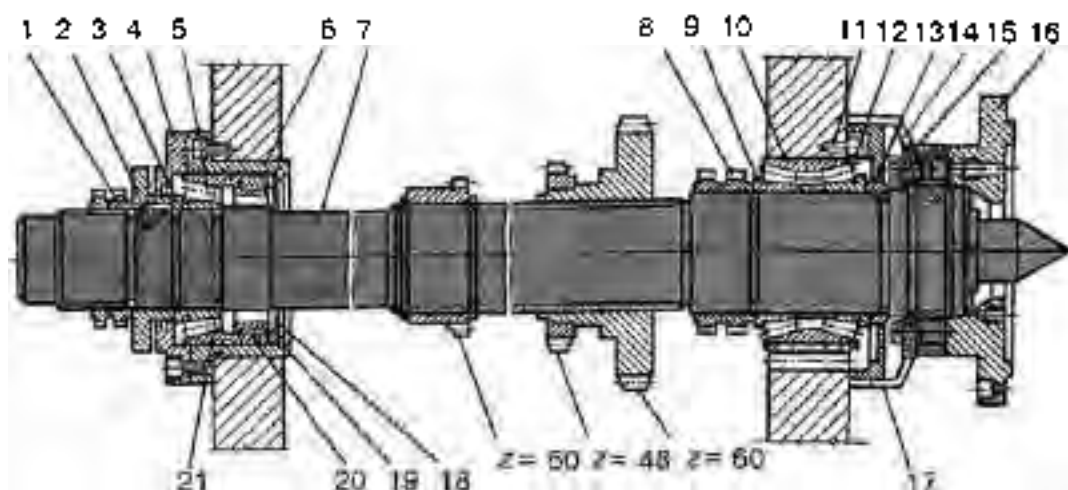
ШПИНДЕЛЬНИЙ ВУЗОЛ ВЕРСТАТА 16К20.
